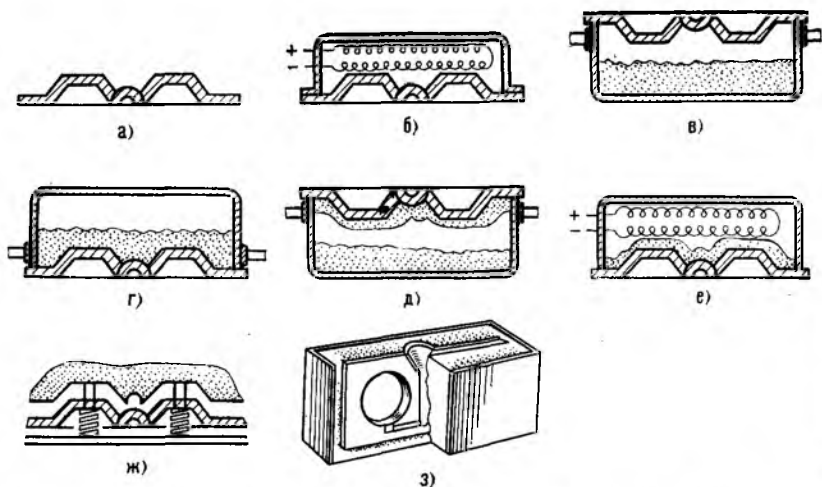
Схема процесса бункерного способа изготовления оболочковых форм
